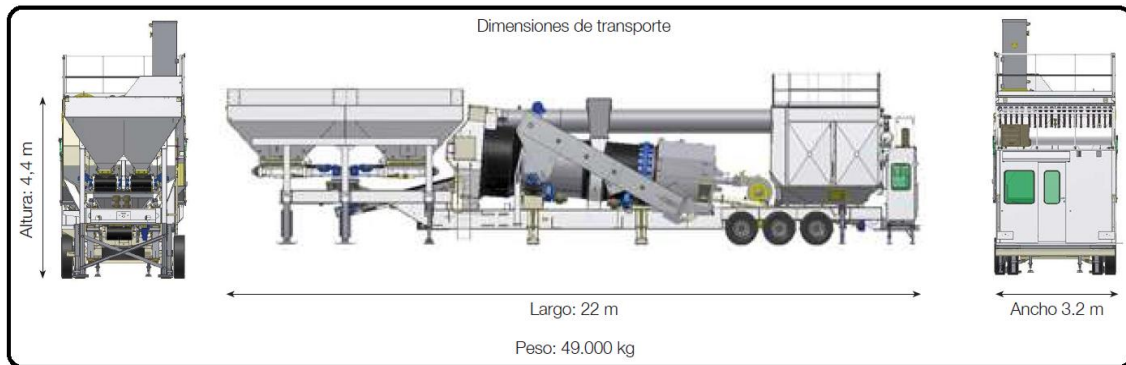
Dimensiones de una planta con producción de hasta 140 t/h.
